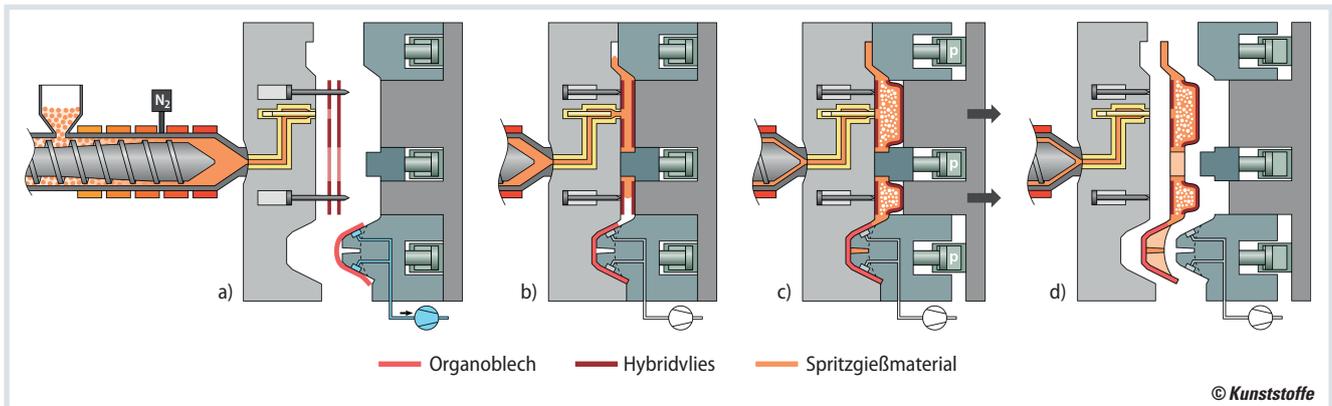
Prozessablauf im Formwerkzeug bei der Fertigung des Technologiedemonstrators: a) Einlegen der aufgewärmten, teilweise gestackten Zuschnitte; b) Einspritzen der Kunststoffschmelze; c) lokaler Expansionshub; d) Bauteil auswerfen (Quelle: ILK/ElringKlinger)
